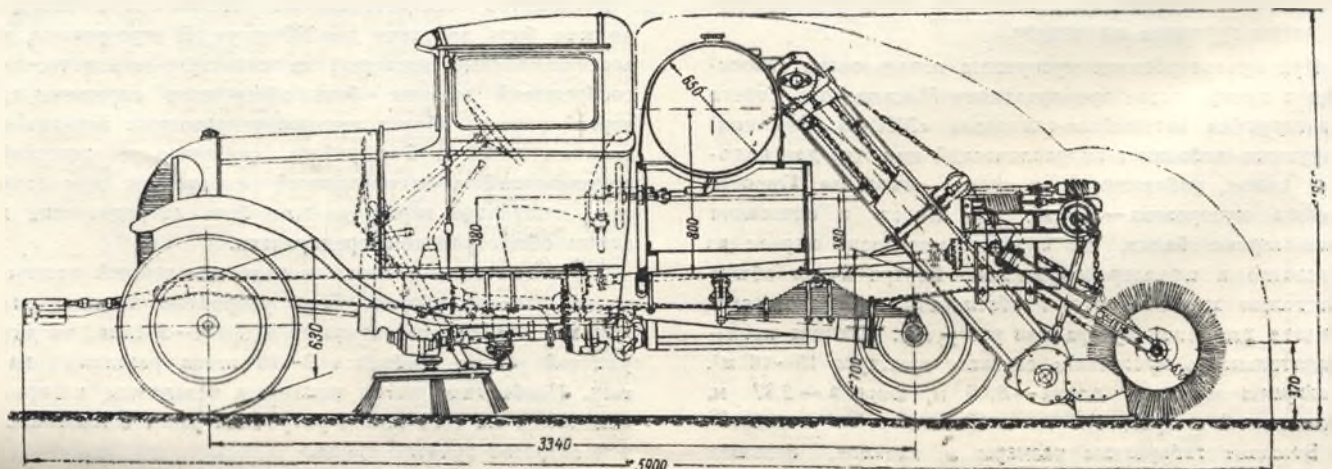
Схема подметально-уборочной машины «ПУ-7». Боковой вид
